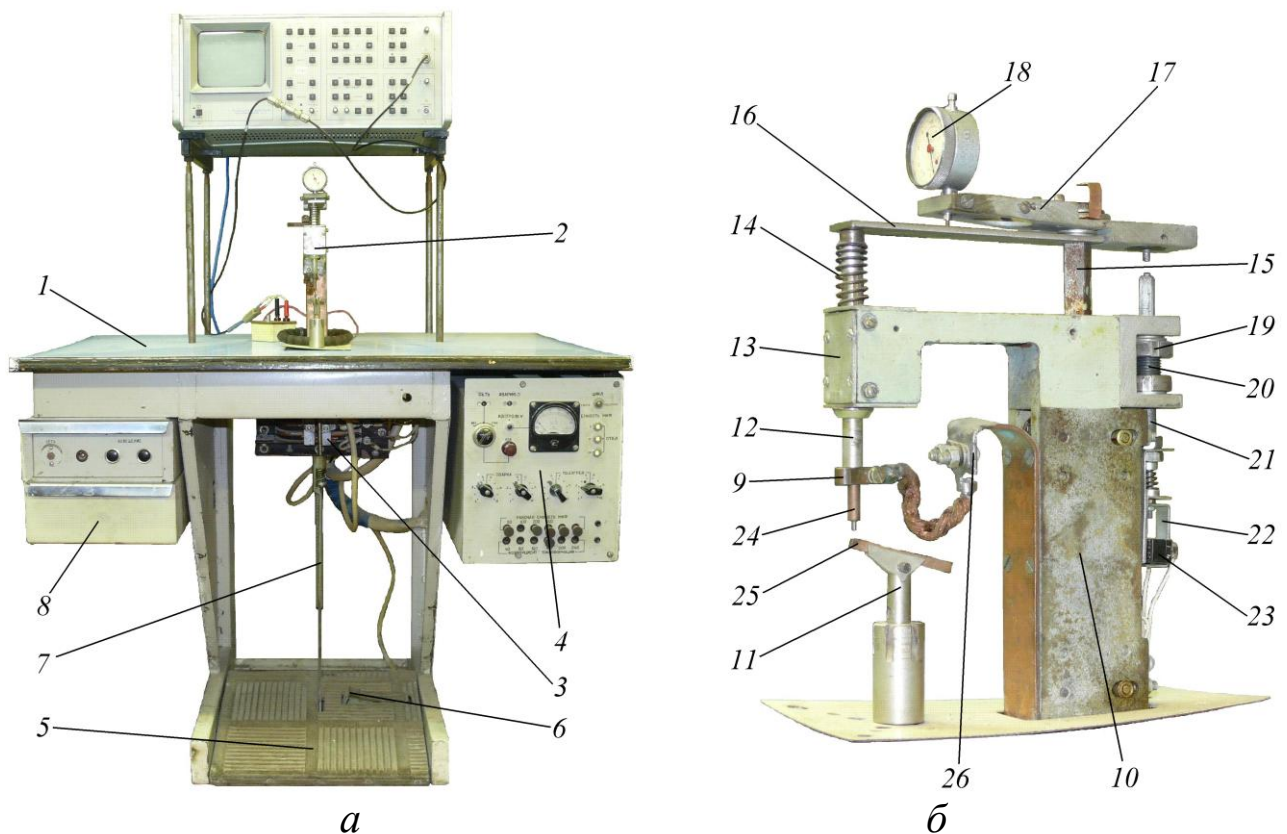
Конденсаторная машина ТКМ-14: *а* – общий вид; *б* – сварочная головка; 1 – монтажный стол; 2 – сварочная головка; 3 – сварочный трансформатор; 4 – конденсаторный дозировщик энергии; 5 – педаль; 6 – переключатель режимов; 7 – тяга; 8 – ящик для инструмента; 9 – верхний электрододержатель; 10 – корпус механизма, создающего сварочное давление; 11 – нижний электрододержатель; 12 – шток; 13 – крышка направляющих с шариками; 14 – возвратная пружина; 15 – шток; 16 – плоская пружина; 17 – кронштейн; 18 – индикатор сварочного давления; 19 – регулировочная гайка; 20 – винт; 21 – штифт; 22 – скоба; 23 – микровыключатель; 24 – электрод верхний; 25 – электрод нижний; 26 – токоподводящая шина
